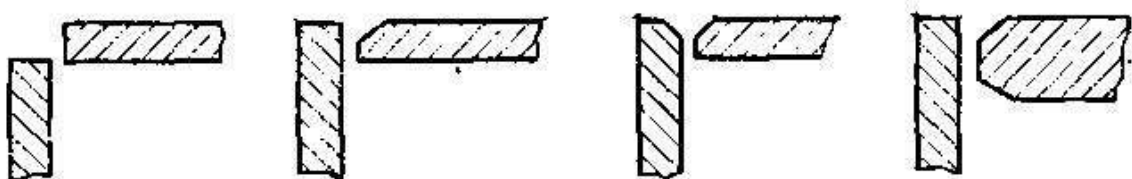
Форма подготовленных кромок под сварку для угловых соединений.
